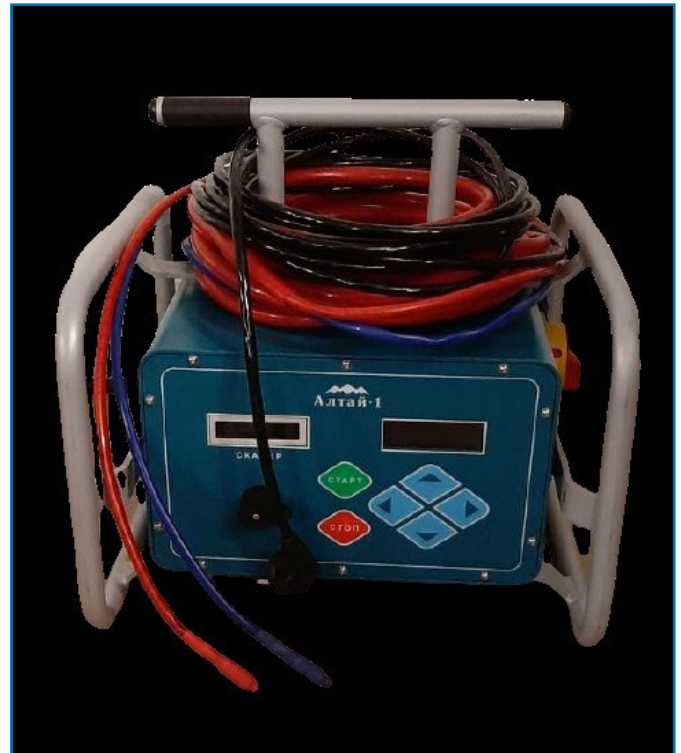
Сварочный аппарат, созданный для терморезисторной сварки труб с ППУ изоляцией большого диаметра.
